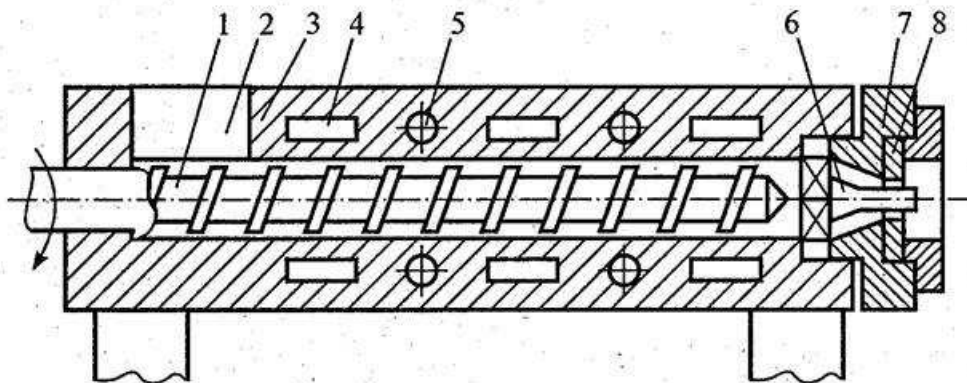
Схема экструдера [16]: 1 – шнек; 2 – загрузочное отверстие; 3 – цилиндр; 4 – водяной или паровой обогрев; 5 – воздушное охлаждение; 6 – сопло; 7 – головка цилиндра; 8 – мундштук
